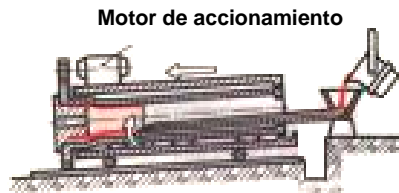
Fundición centrífuga – colada en moldes permanentes
